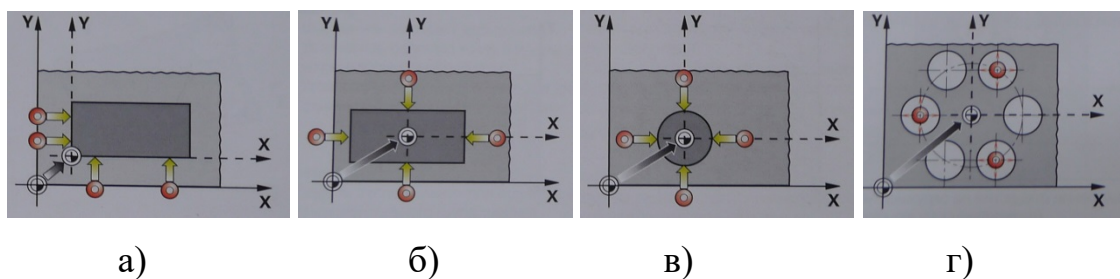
Визначення опорних точок для за допомогою вимірювального щупа: а – зовнішній кут; б – центр прямокутної заготовки; в – центр циліндричної заготовки; г – центр отворів, виконаних по колу
